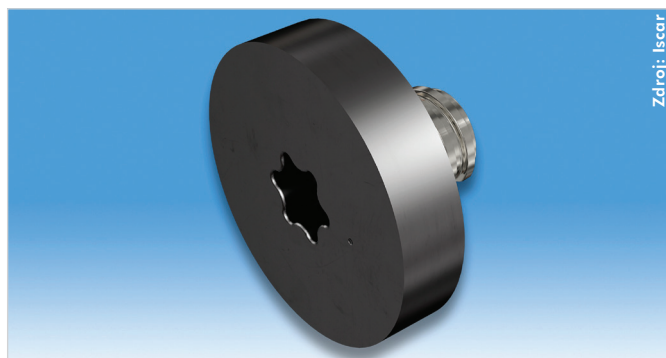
Široká škála vyměnitelných hlavice, stopek, adaptérů, prodloužení a redukci tvoří univerzální modulární systém Multi-Master.
